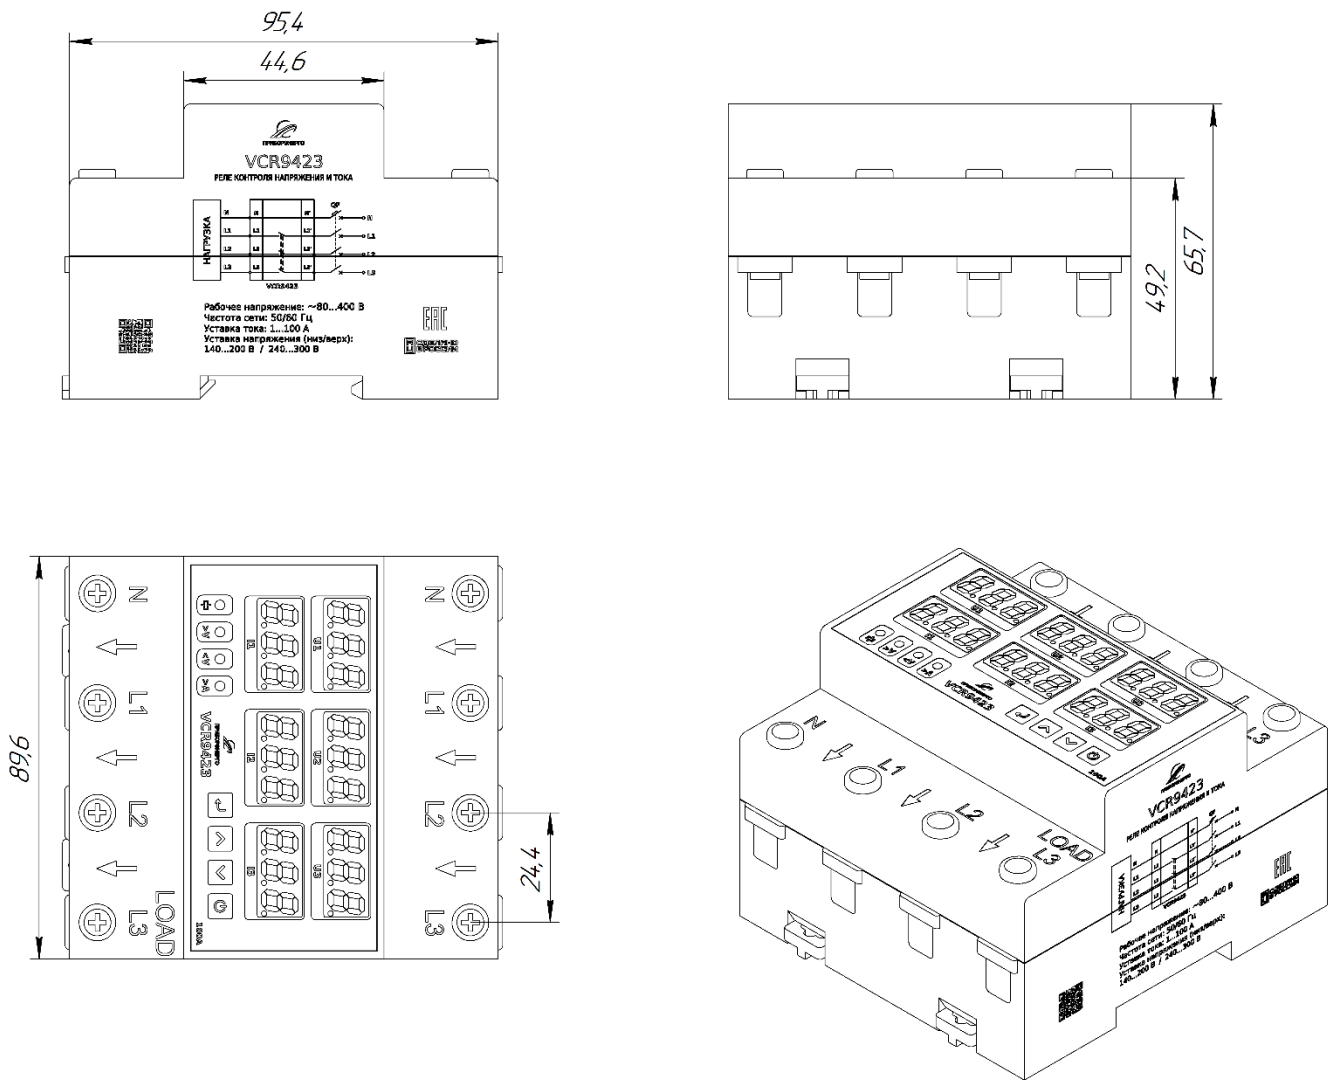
Габаритные размеры реле контроля напряжения и тока VCR9423
